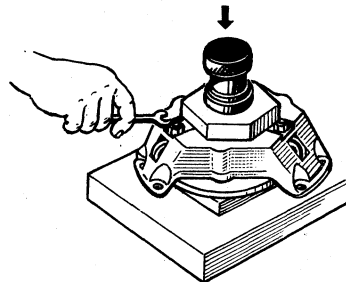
Разборка и сборка кожуха сцепления с цилиндрическими нажимными пружинами
